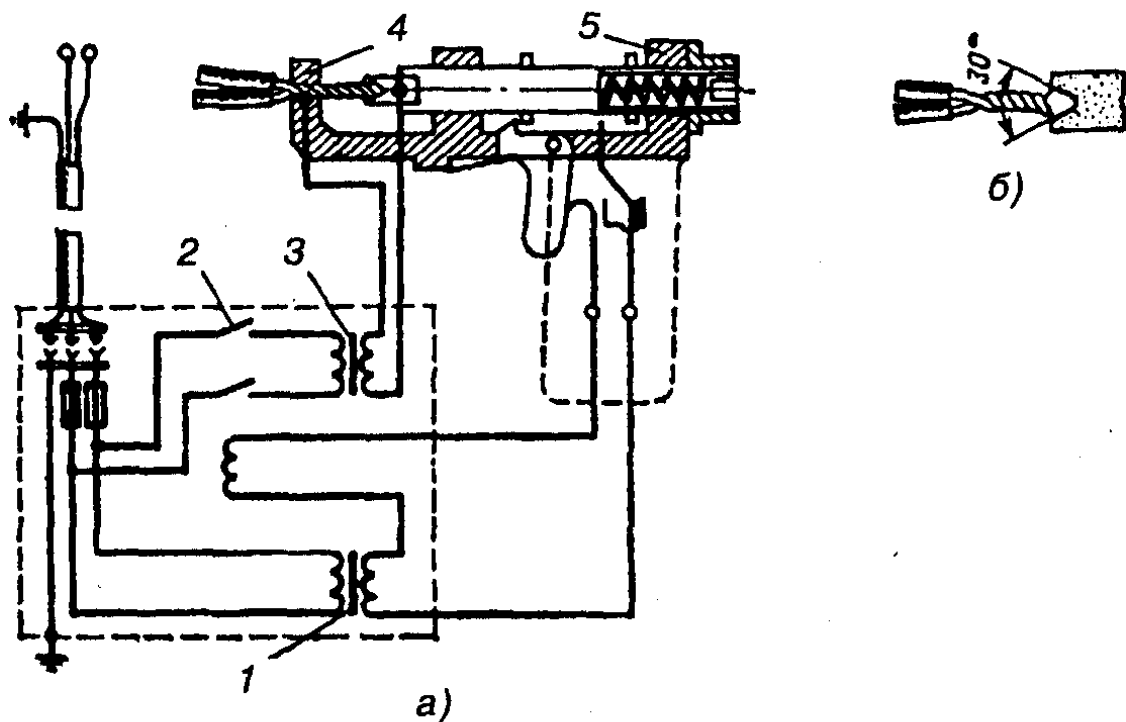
Схема автоматической сварки контактным разогревом алюминиевых жил с применением аппарата ВКЗ:
